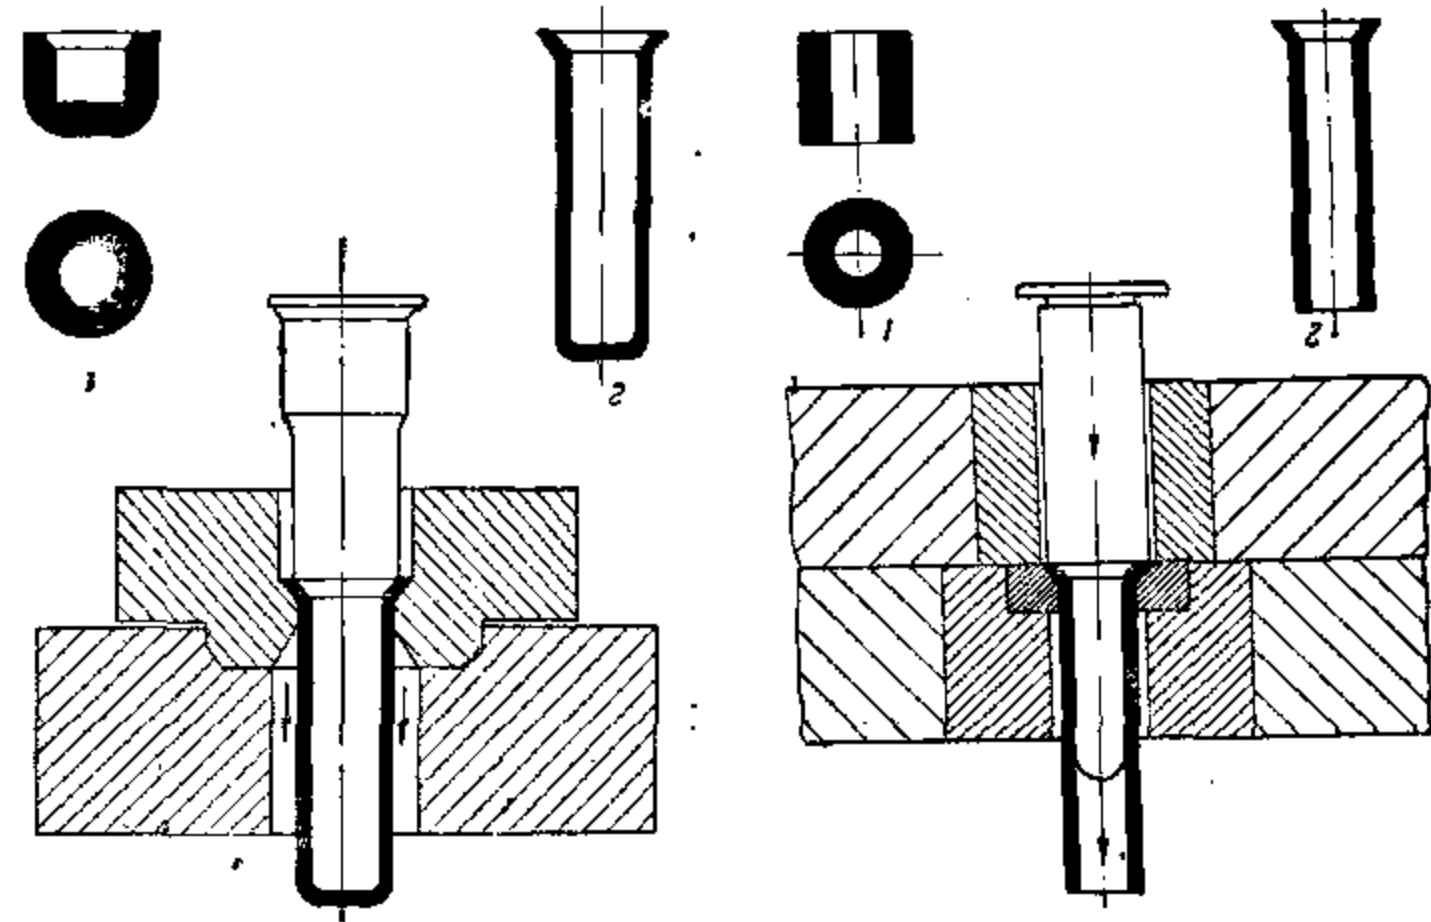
Прямой способ выдавливания из полой толстостенной заготовки 1 цилиндрического изделия 2
